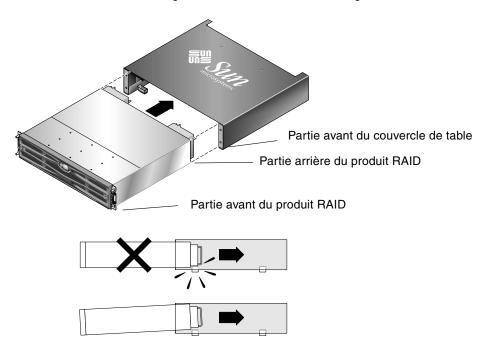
Coulissement du châssis dans le couvercle de table
